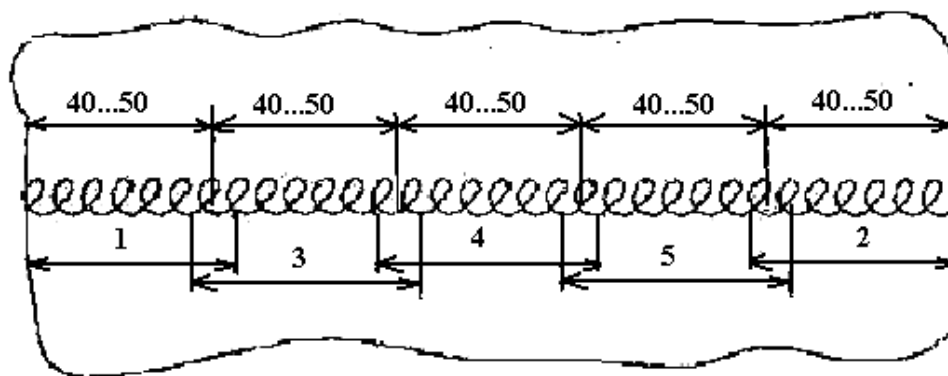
Последовательность наложения швов при сварке чугуна: 1...5 - номера участков
